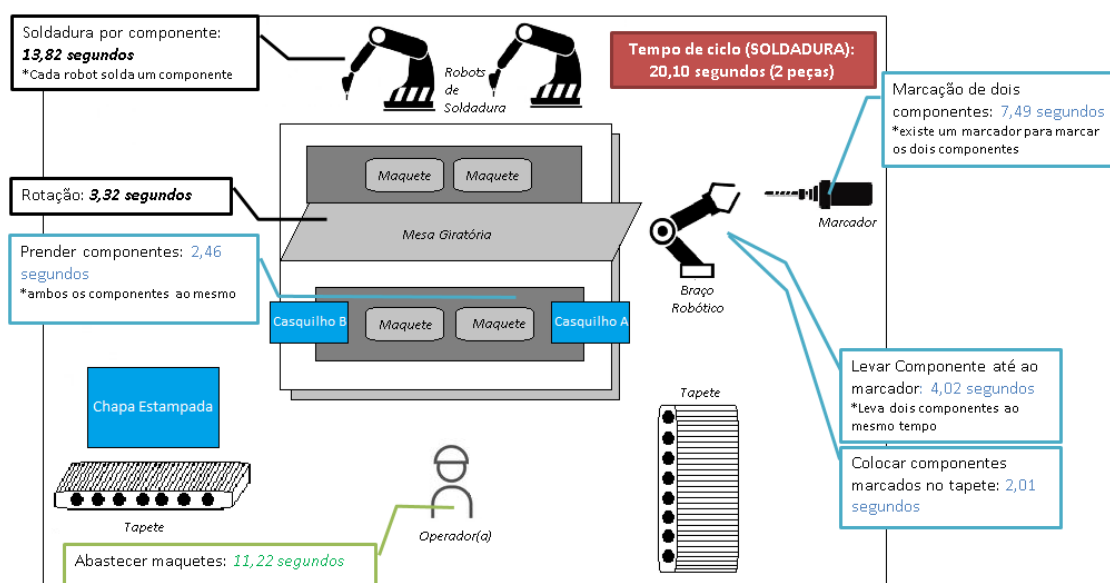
Representação do cenário inicial da célula de soldadura
